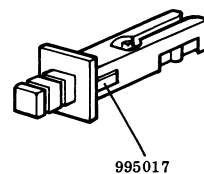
Arm, vender, uavhengig utløser med 2 slepekontakter.
